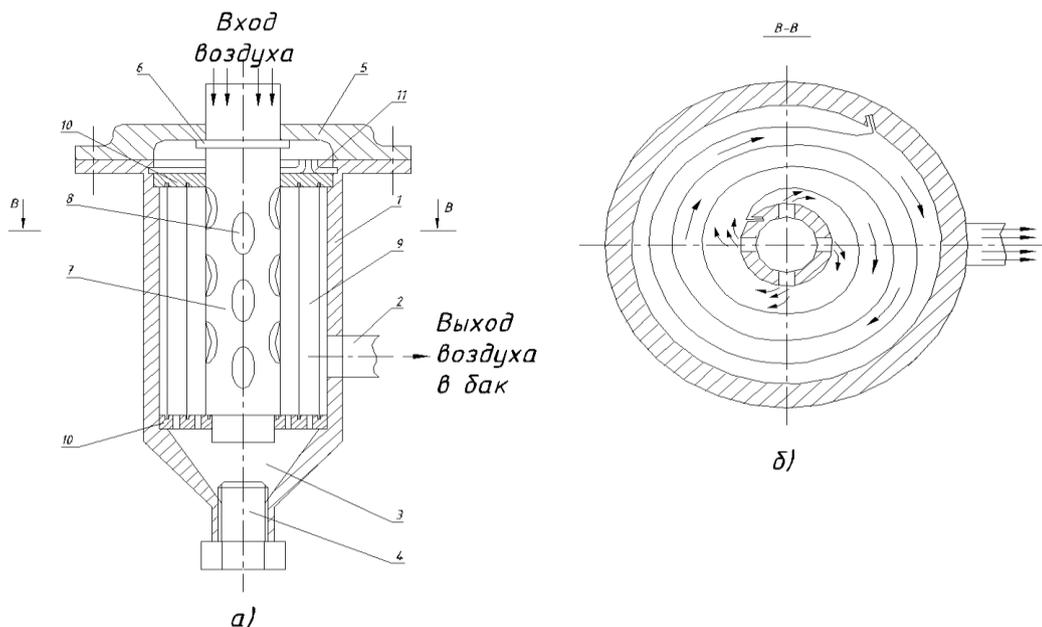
Масляный пылеуловитель (патент РФ № 2257487): а) – сборочный чертеж; б) – вид устройства архимедовой спирали
